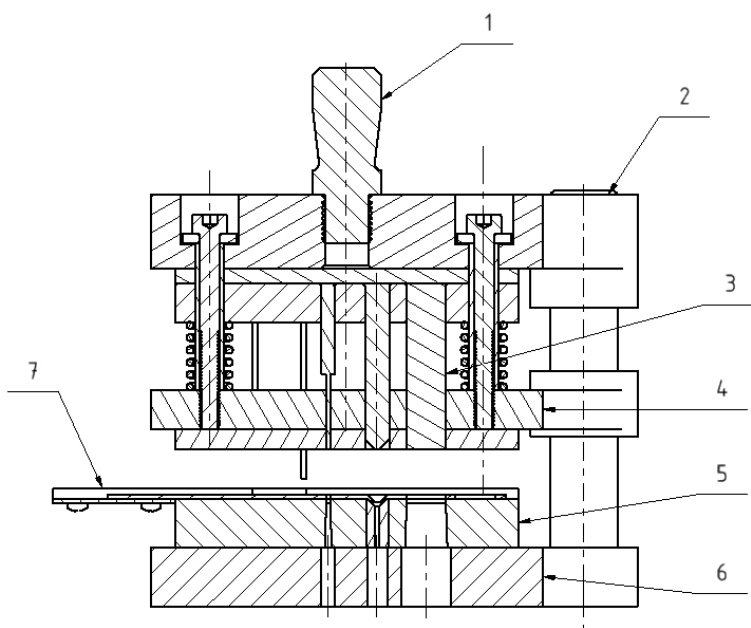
Folgeverbund-Werkzeug für eine Abdeckplatte
